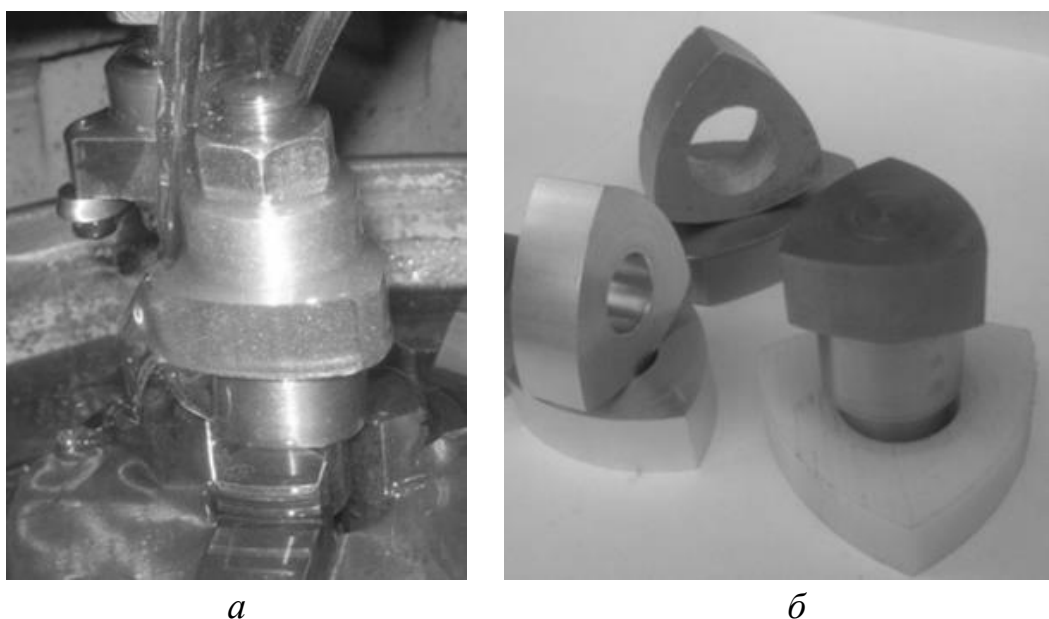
Рабочая зона станка (а) и образцы обработанных изделий (б)
